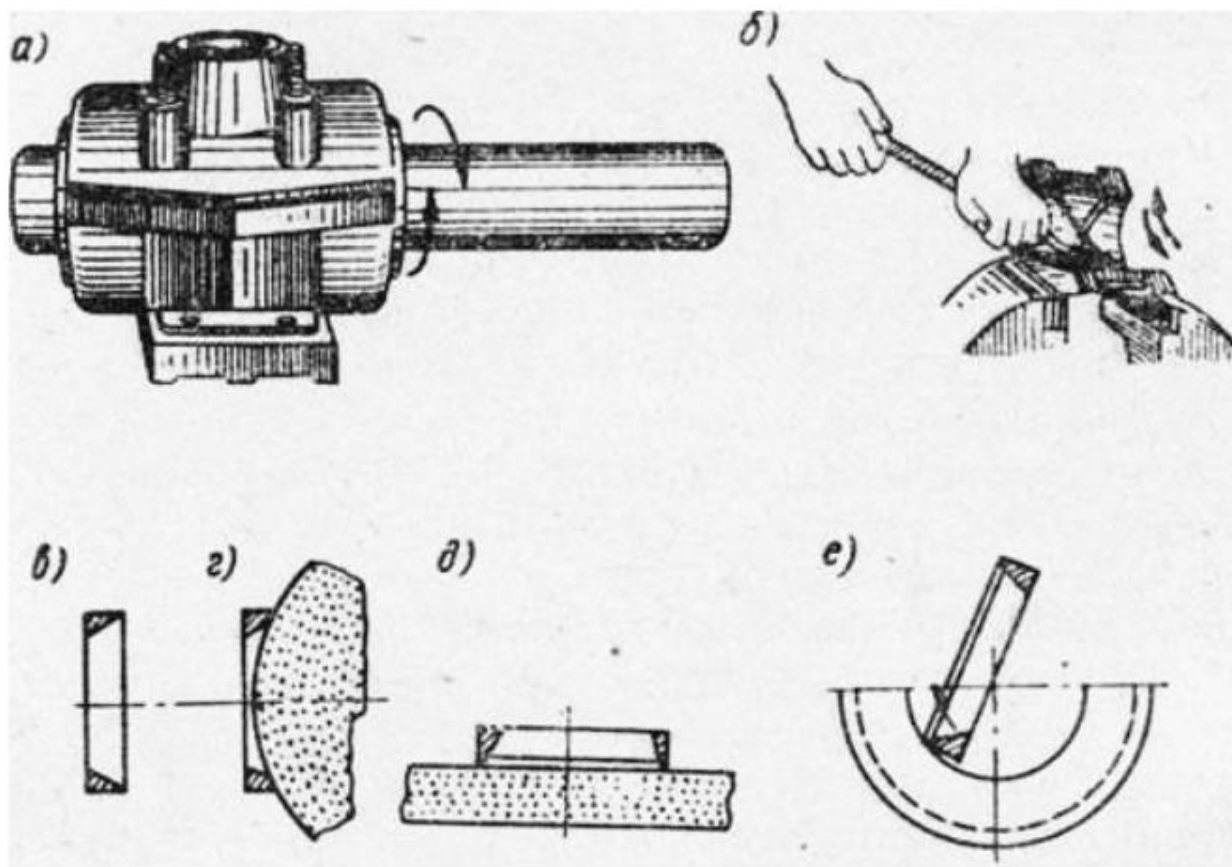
Приемы шабрения вкладышей подшипников (а, б); специальные шаберы-кольца для шабрения вкладышей подшипников (в, г, д, е)
